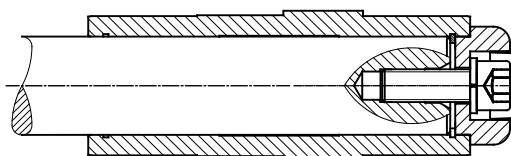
Mecanismul de transmisie fixat cu elementul de fixare pe arborele fără umăr de sprijin
